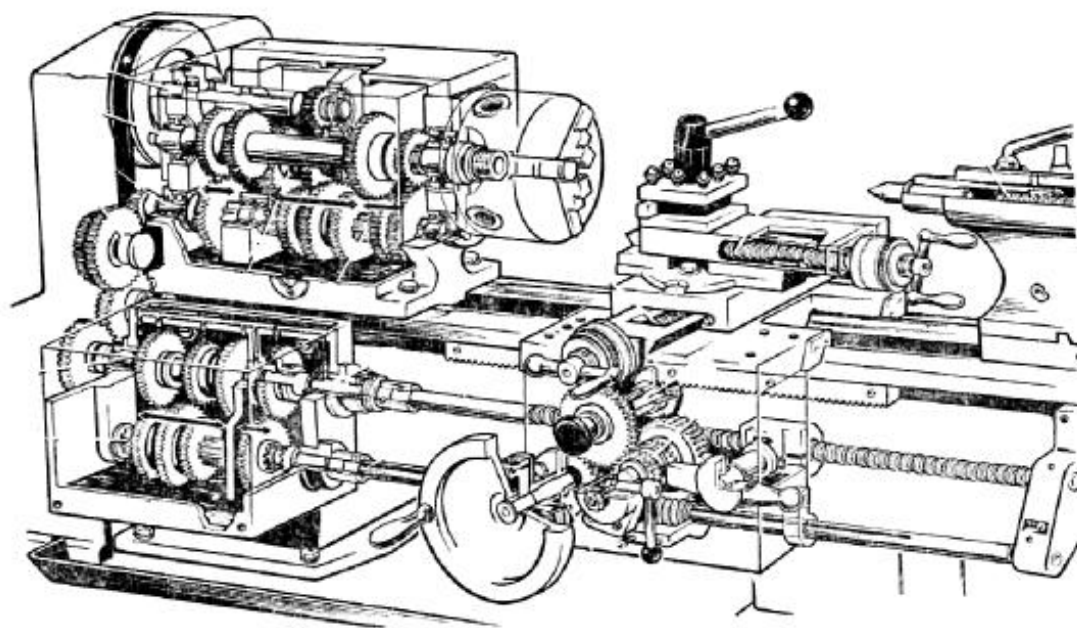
Механізми токарно-гвинторізного верстата ТВ-6
